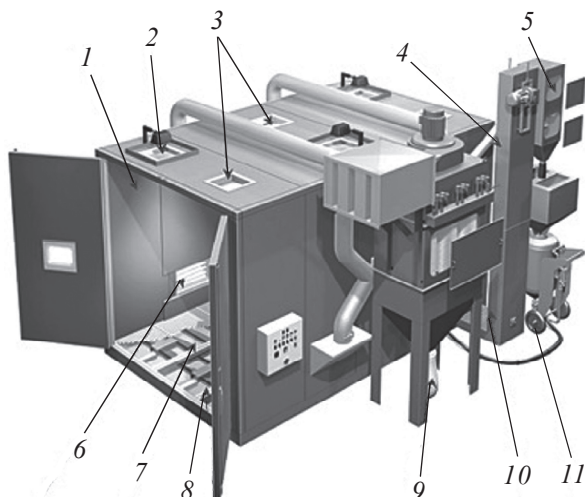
Чистка профилей металлопроката в дробеструйной камере с системой сбора дроби PULSOMATIC:
